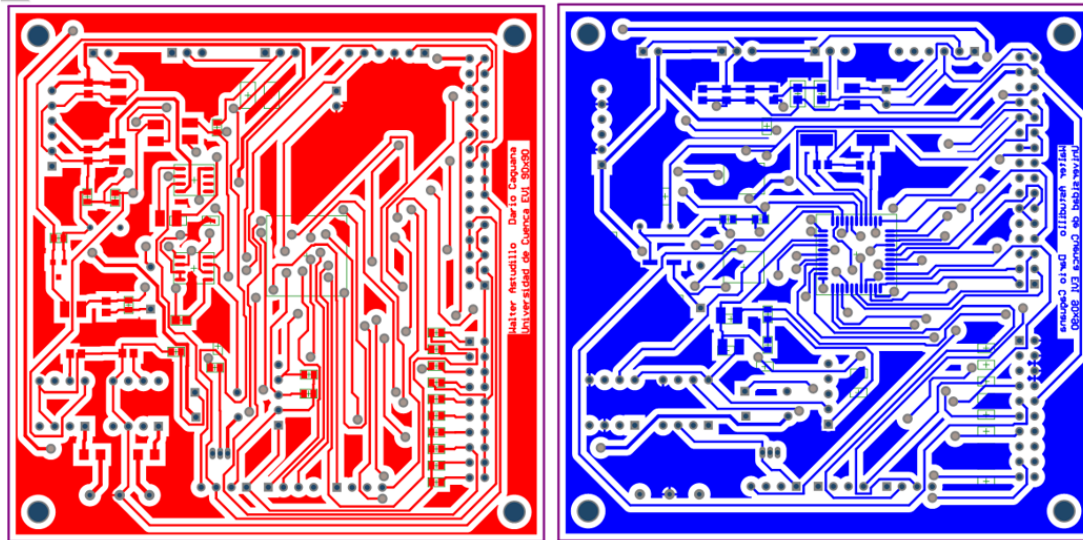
Component Side y Bottom Layer del circuito impreso.
